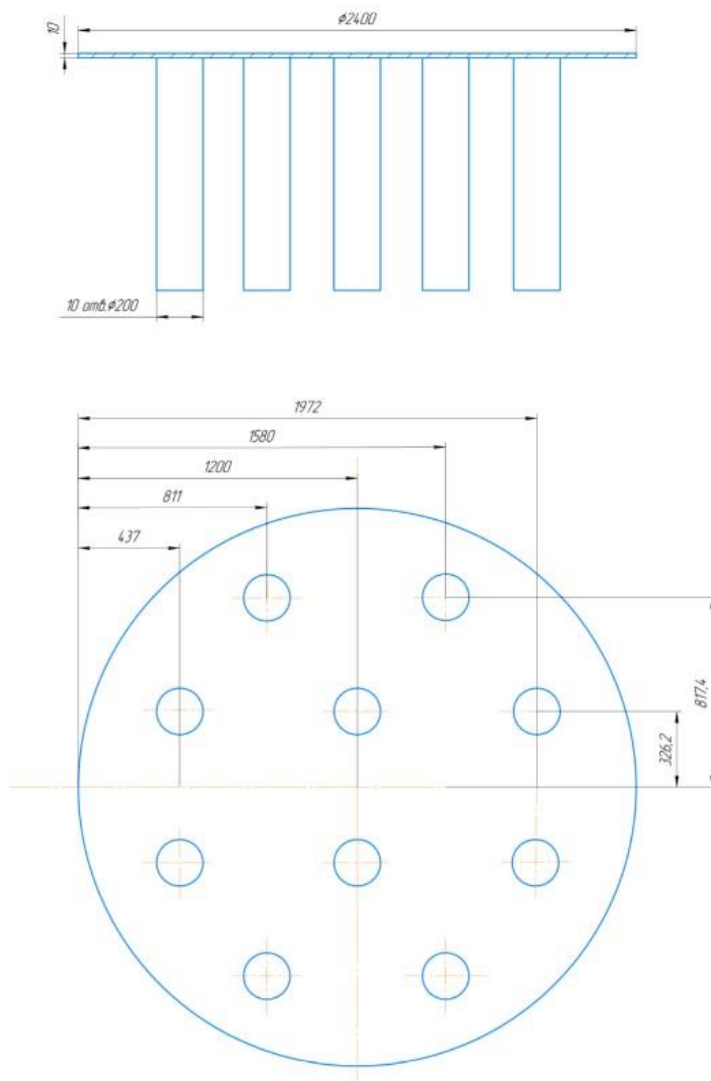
Чертеж верхней трубной решетки с выходными трубками
